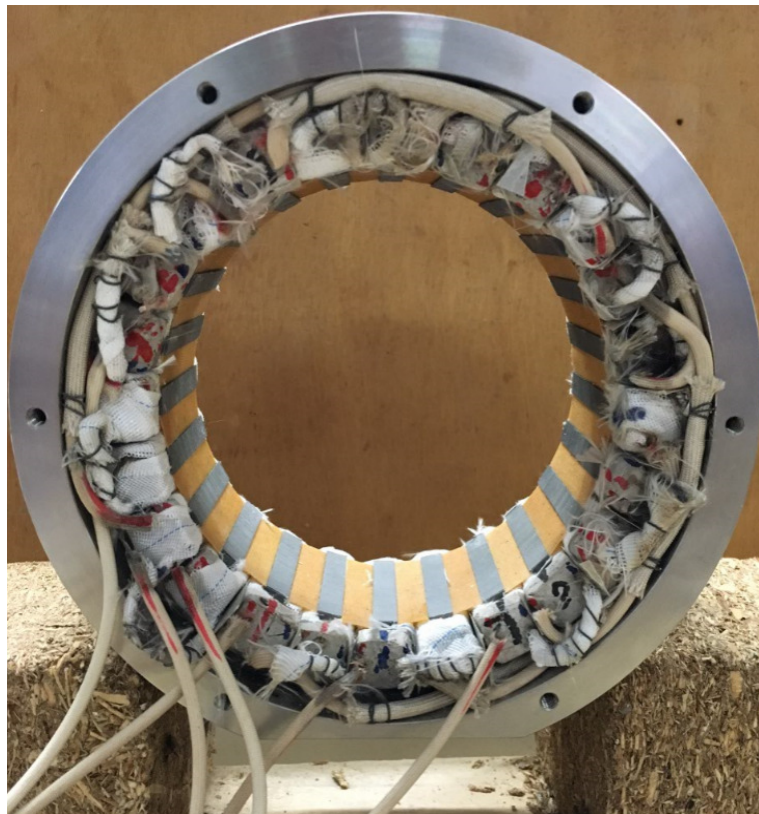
Le stator avec les bobines assemblées , vue générale.
